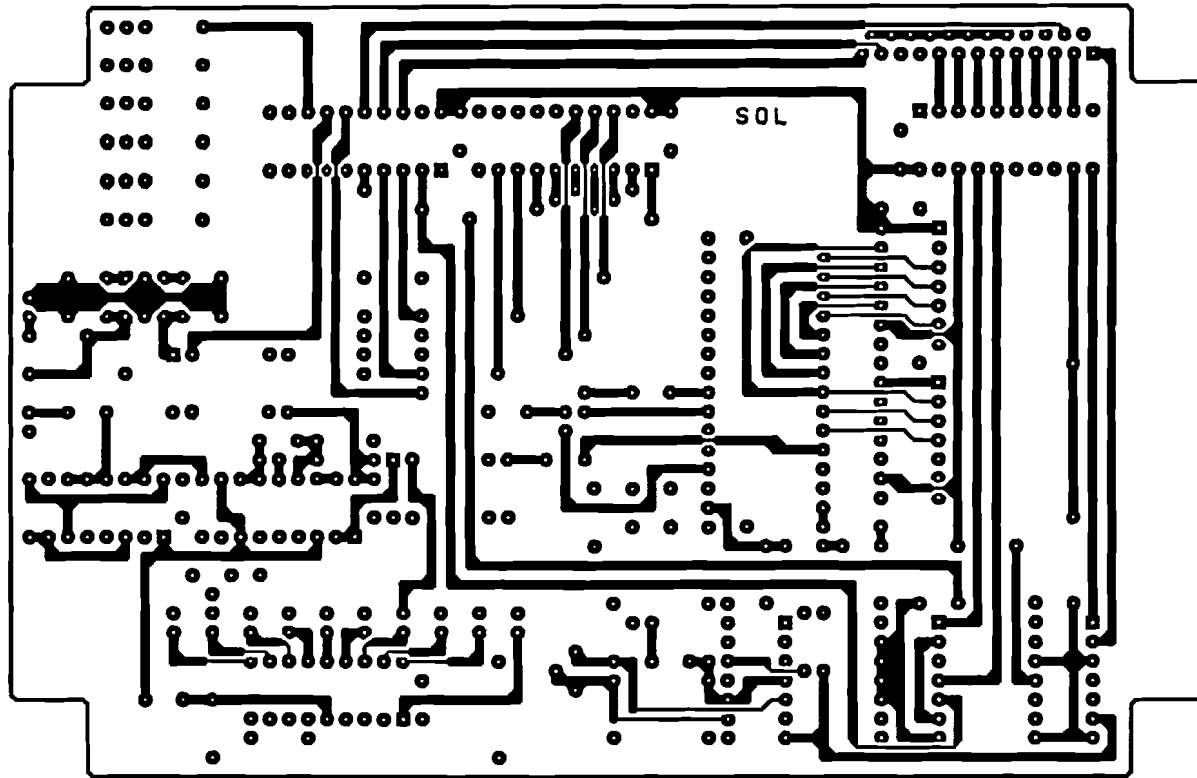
Printlayout van de ISD10xx/25xx programmer, solder layer.
